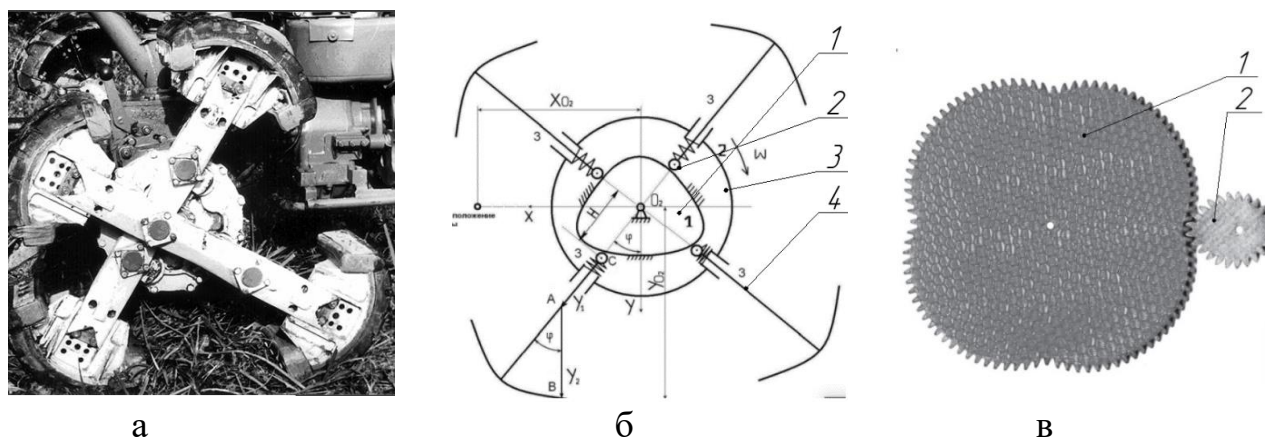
Конструкция колёсно-шагающего движителя
